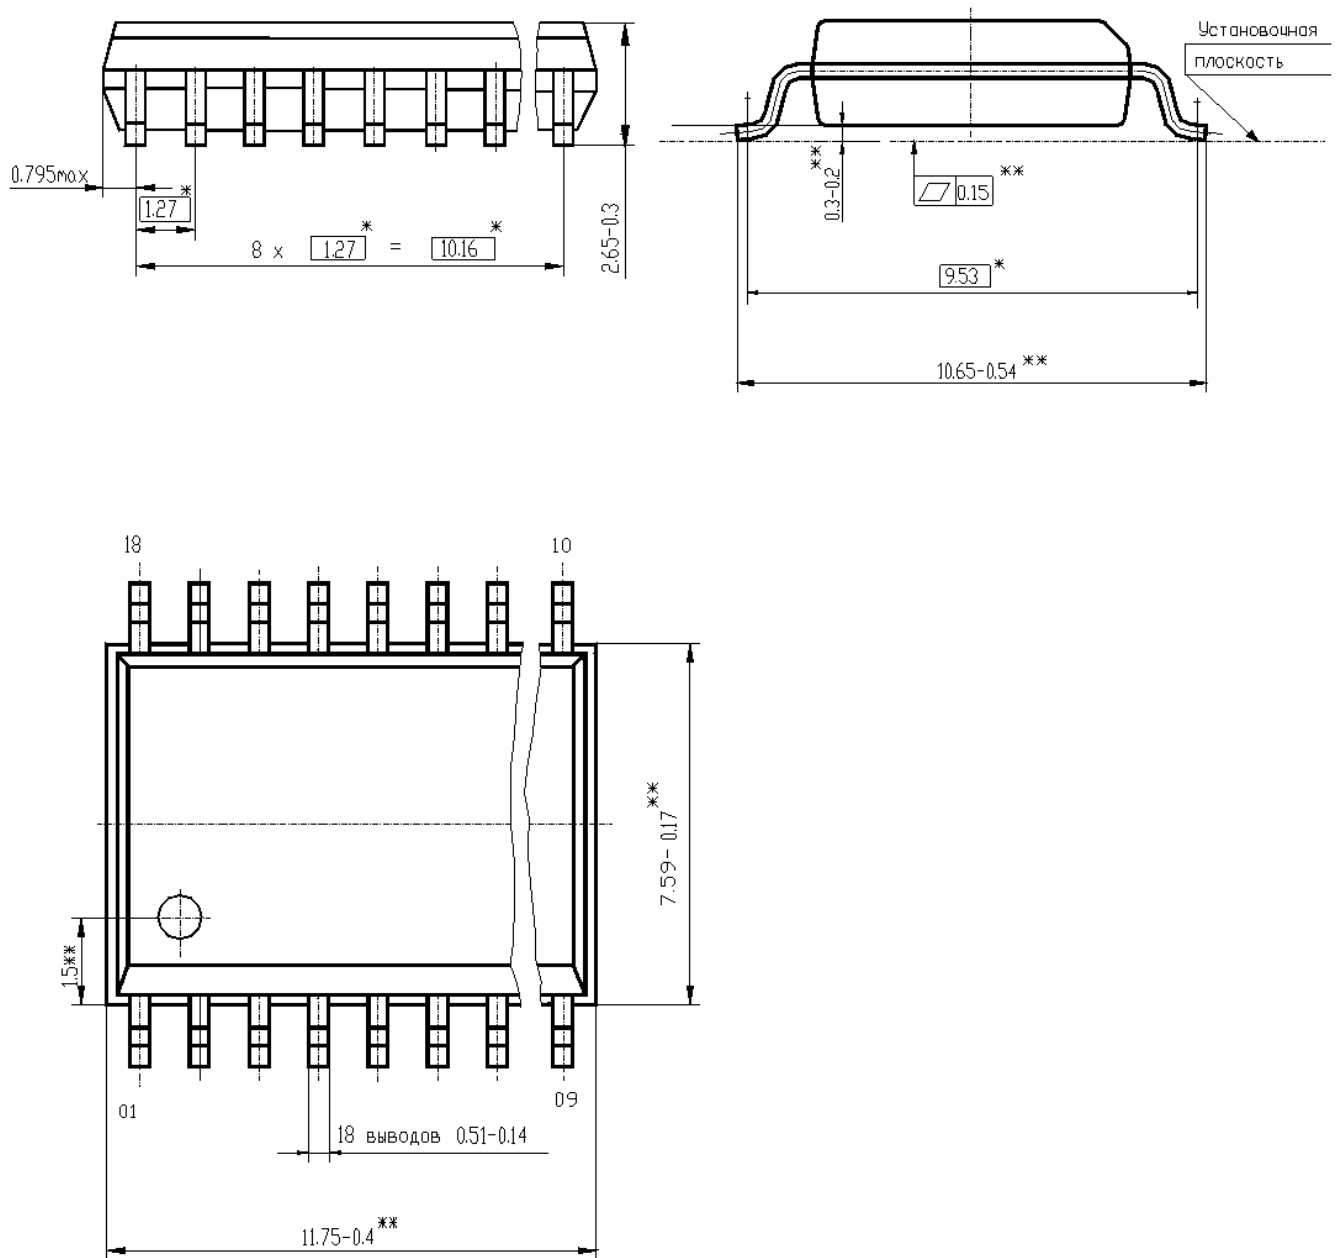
Габаритный чертеж корпуса MS-013AB
